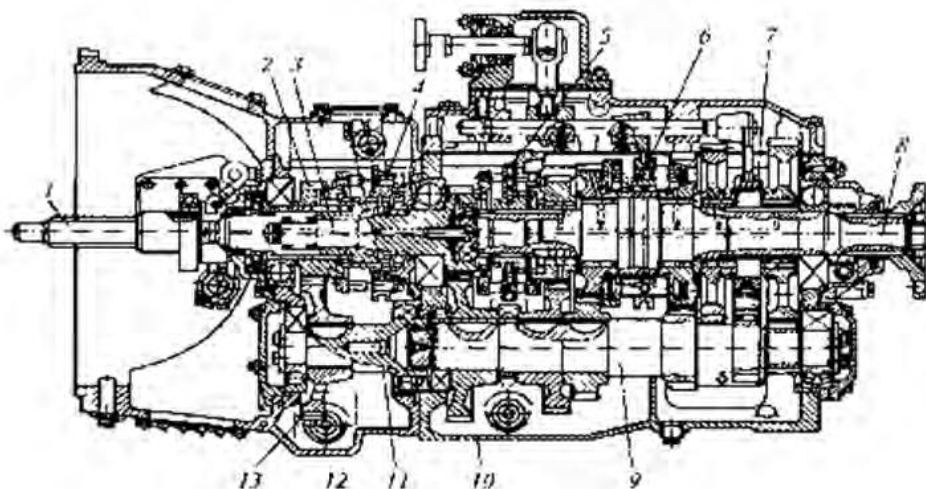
Коробка передач грузового автомобиля КамАЗ с делителем:
